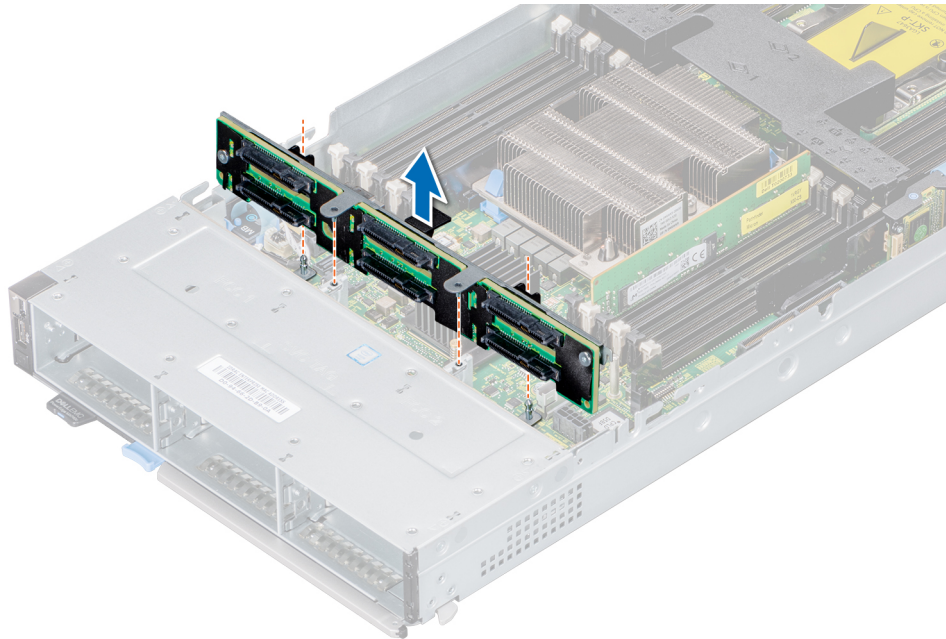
Entfernen der Laufwerks-Rückwandplatine
